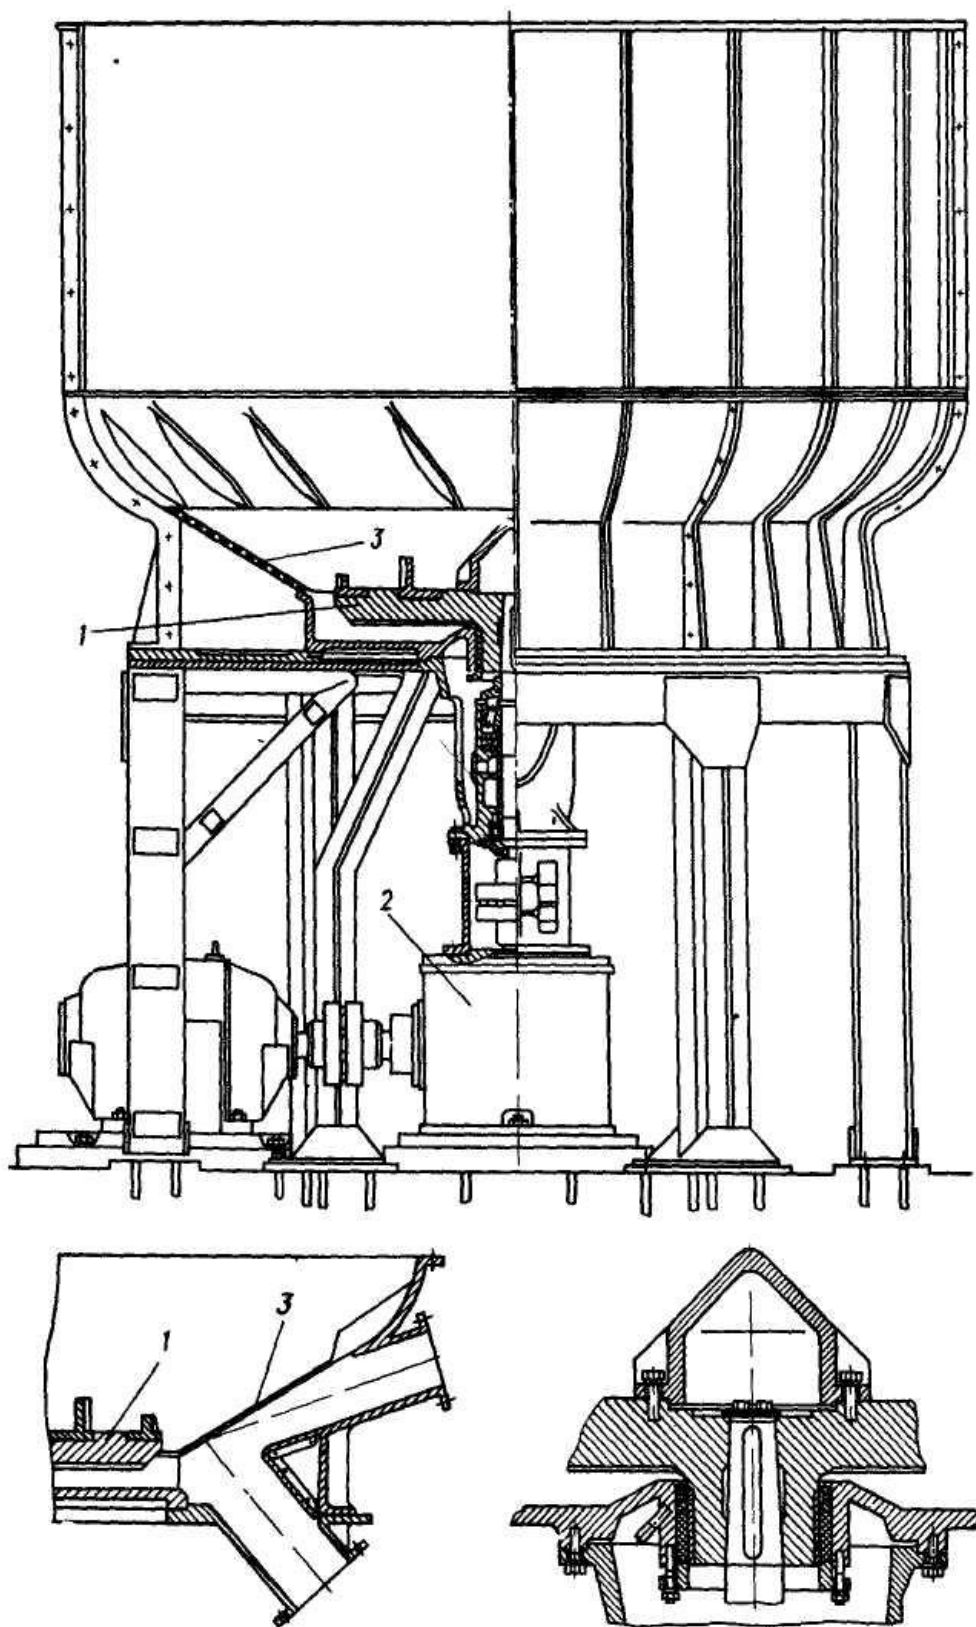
Гидроразбиватель открытого типа с редукторным приводом:
